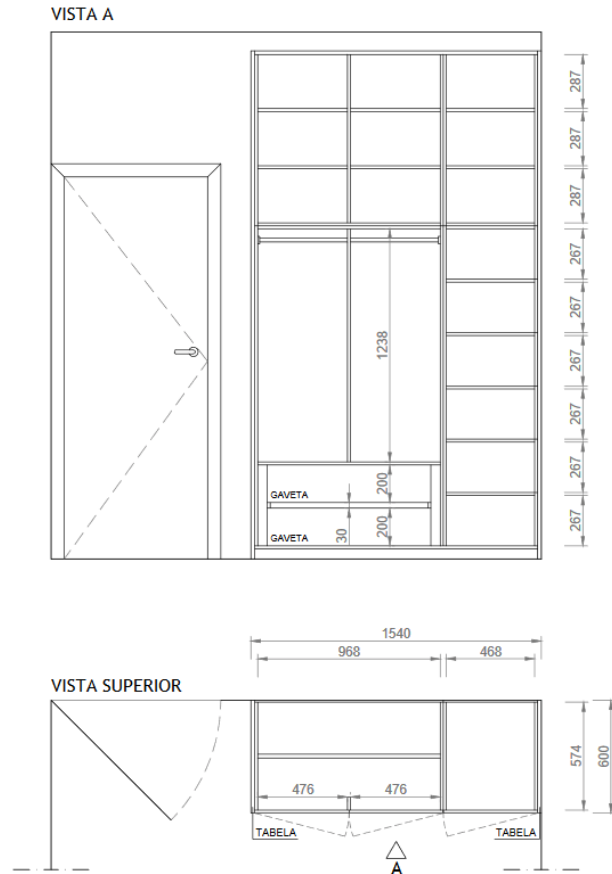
Desenho técnico. Cotagem geral do roupeiro.
